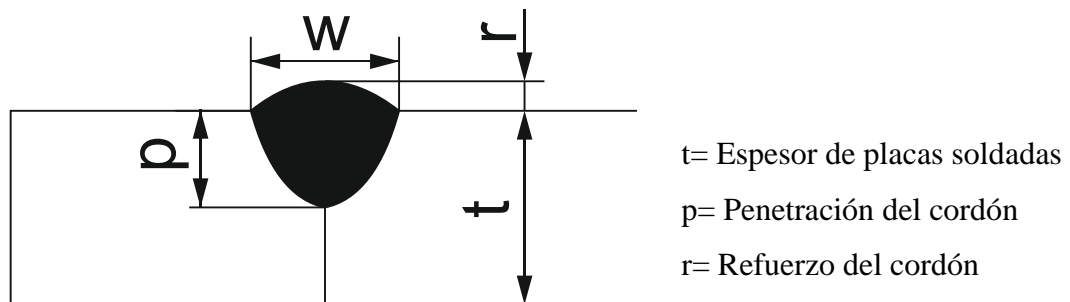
Parámetros del cordón de soldadura [15].
